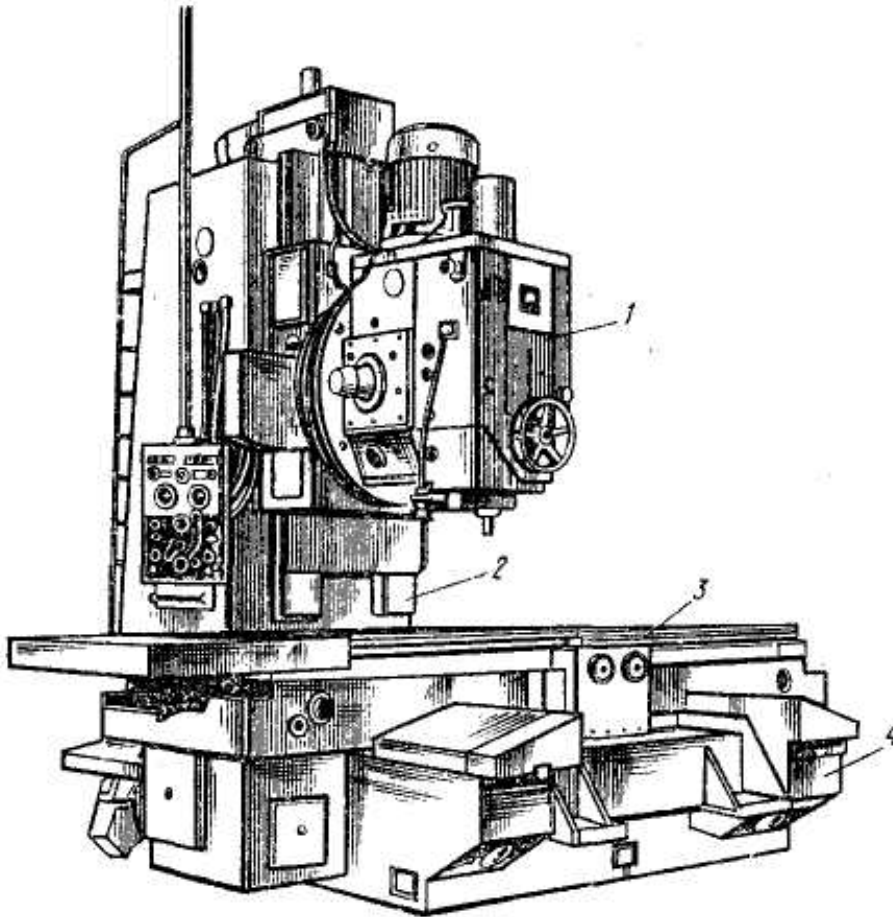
Бесконсольный фрезерный станок: 1 – шпиндельная головка; 2 – стойка; 3 – стол; 4 – массивная станина
